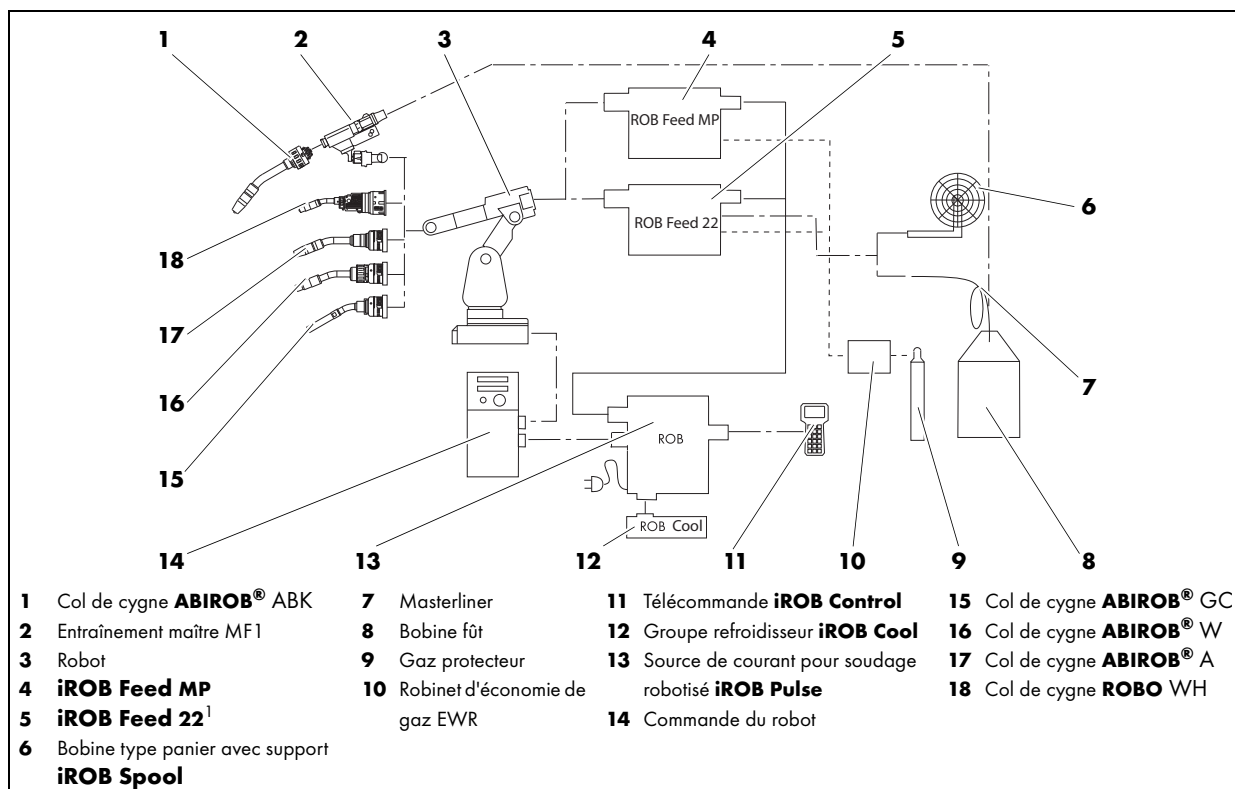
Éléments de l'équipement de soudage robotisé
